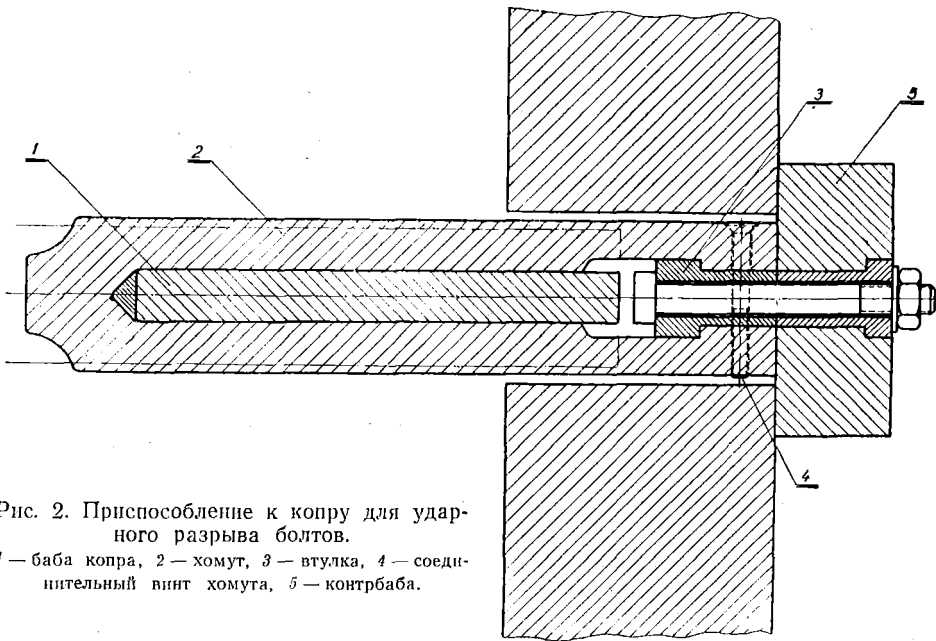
Приспособление к копру для ударного разрыва болтов.
